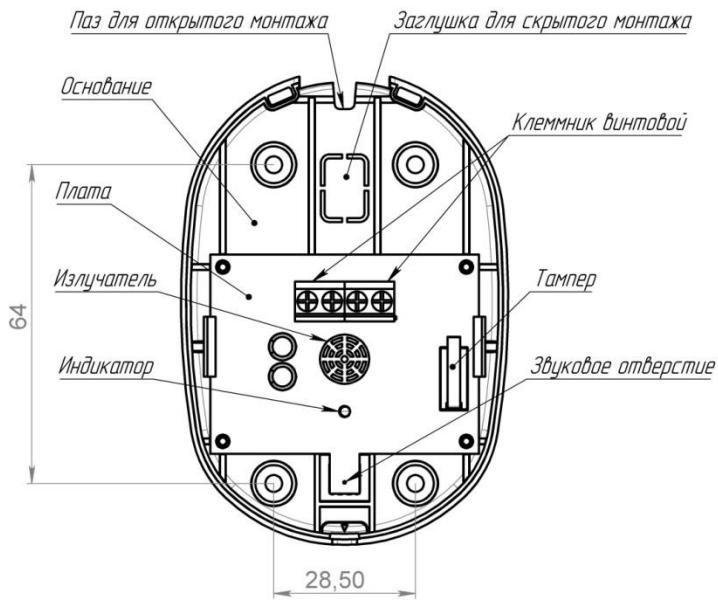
Конструкция и установочные размеры извещателя.
